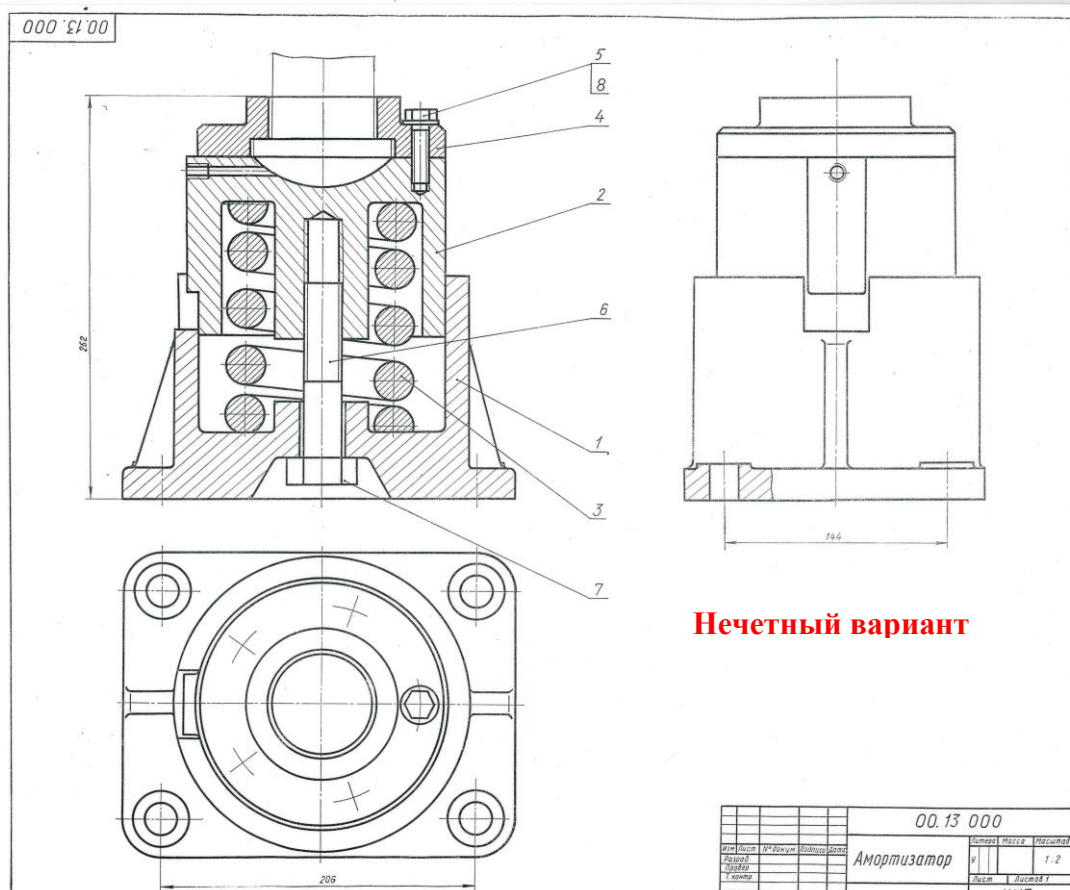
Сборочный чертеж Амортизатор (для нечетных вариантов)
